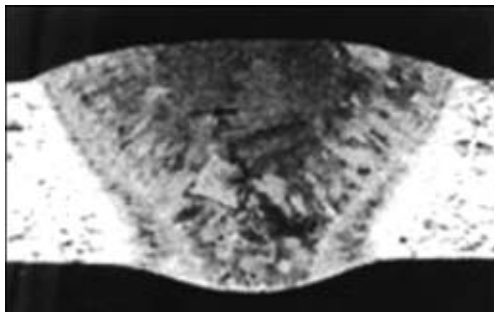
Макрошлиф (X8) соединения сплава АМг3, полученного гибридным способом сварки с подачей присадочной проволоки
